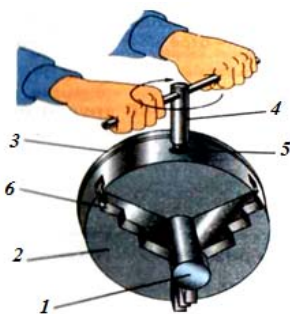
Установка заготовок в трехкулачковый патрон:
